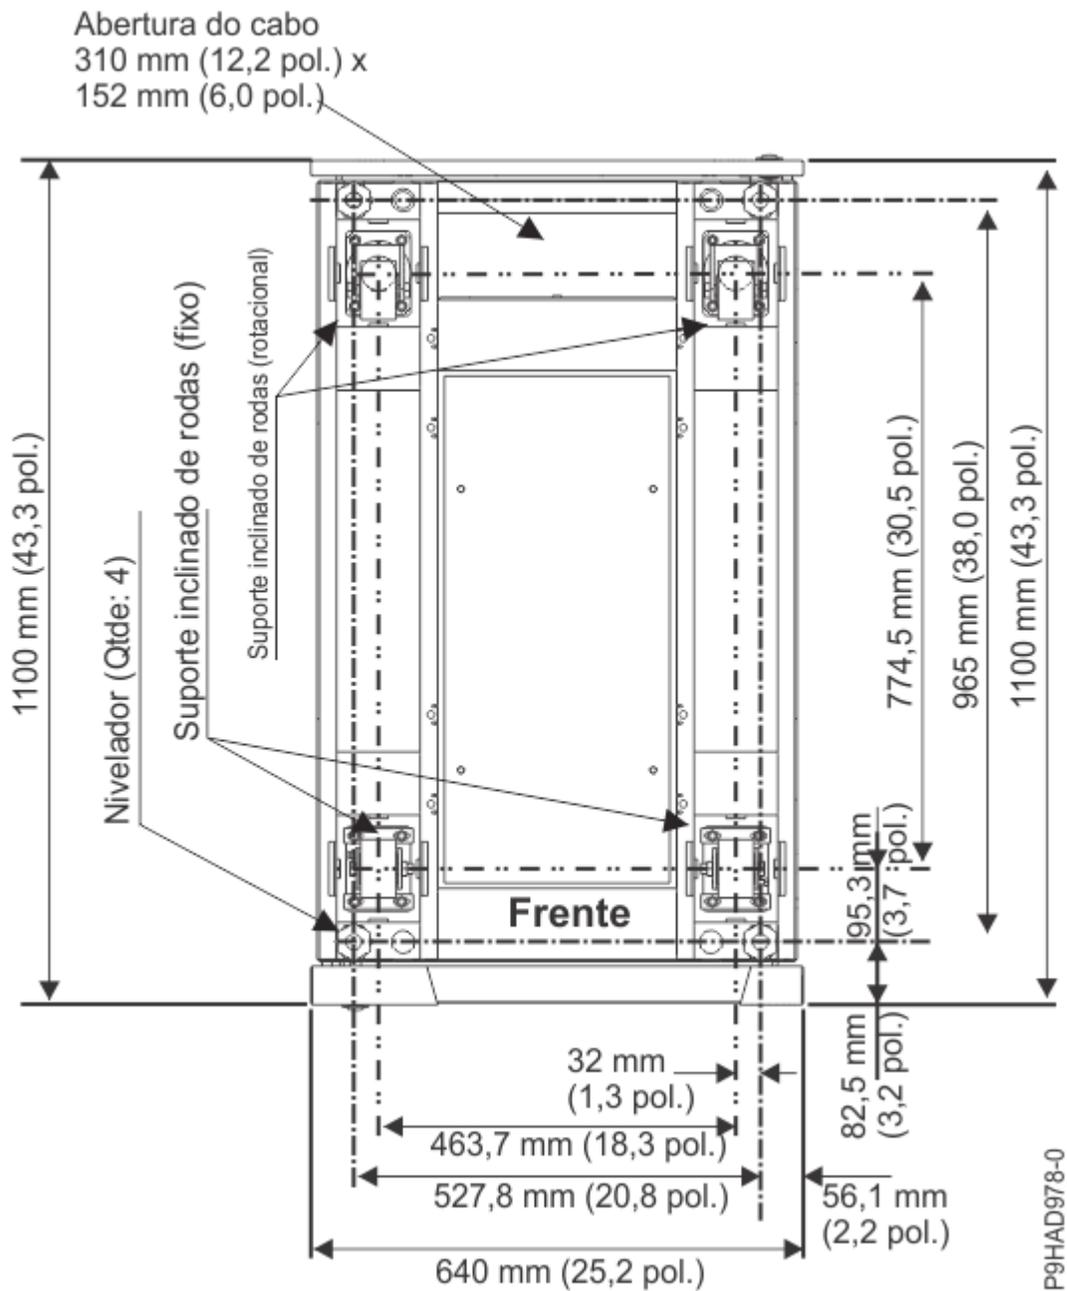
Locais do suporte inclinado de rodas e do nivelador
